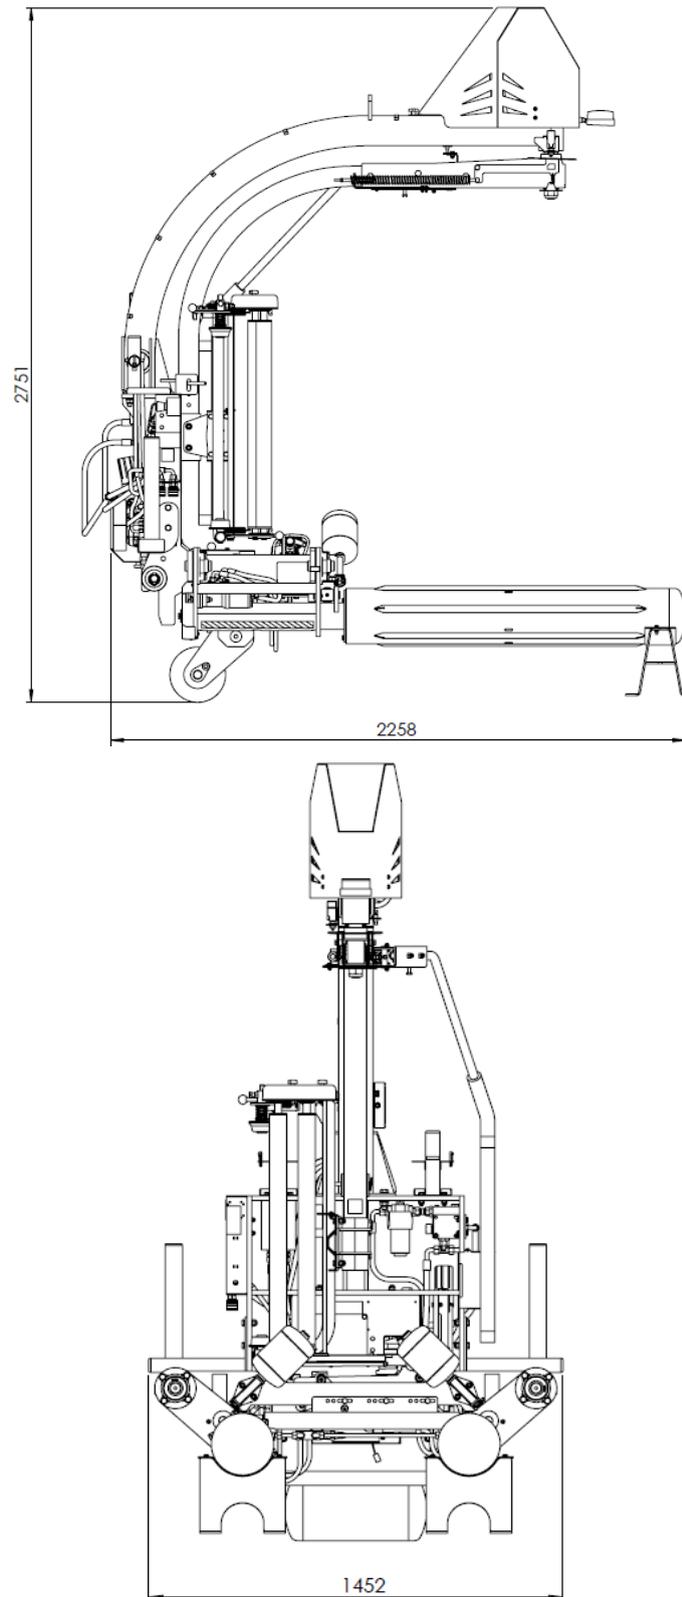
Dimensiones de la encintadora en la posición de transporte.
